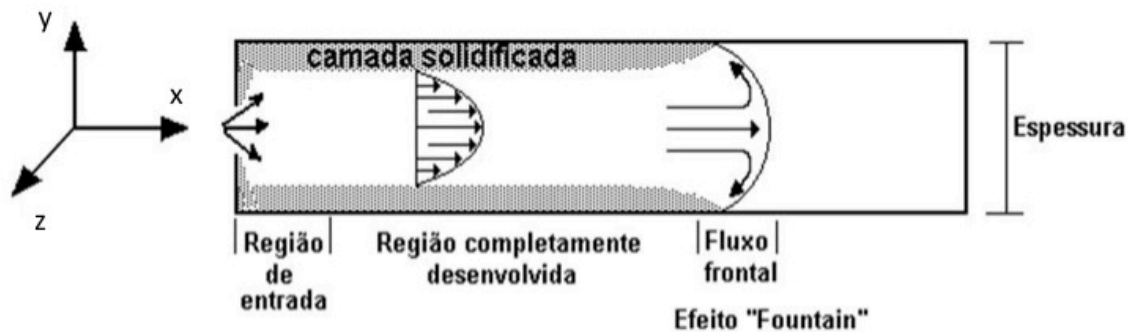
Fluxo dentro do molde durante o processo de moldagem por injeção [71].
